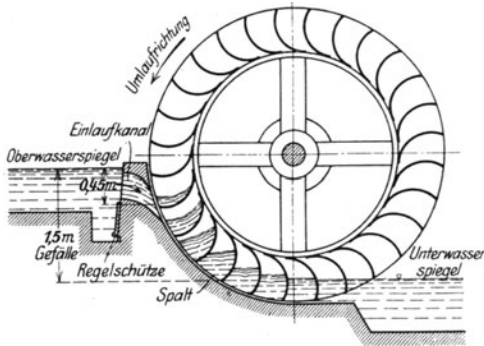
Richtig gebautes mittelschlächtiges Wasserrad.
